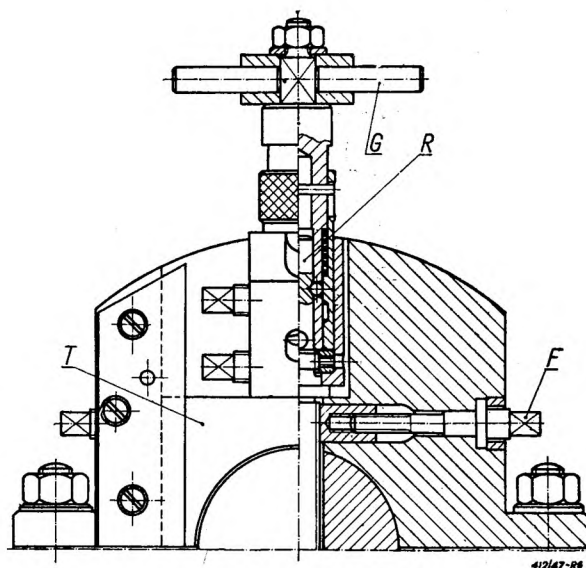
Głowica nożowa do planowania powierzchni czołowych.
